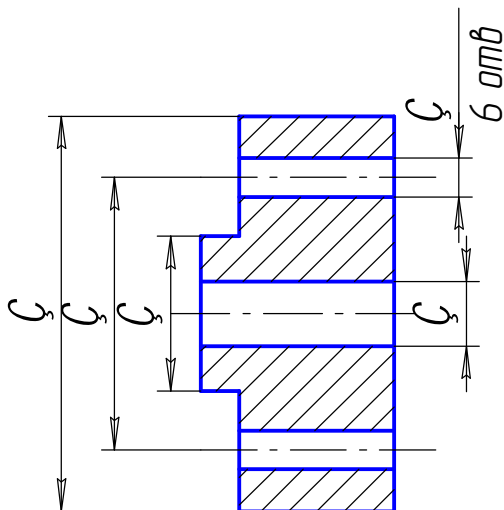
Чертеж диска с равномерно расположенными цилиндрическими отверстиями.
